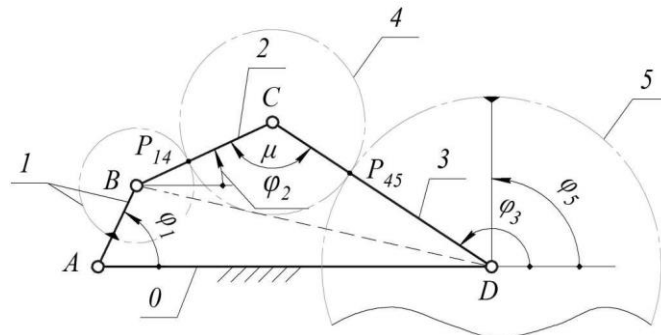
Зубчато-рычажный механизм Роттенбахера
